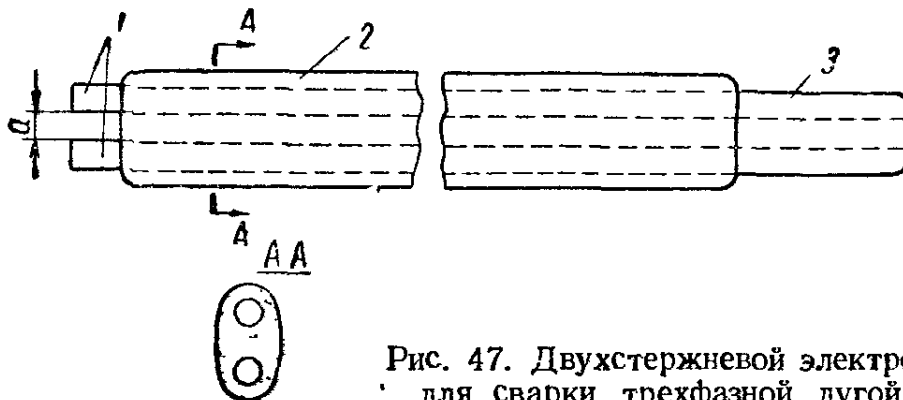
Двухстержневой электрод для сварки трехфазной дугой
